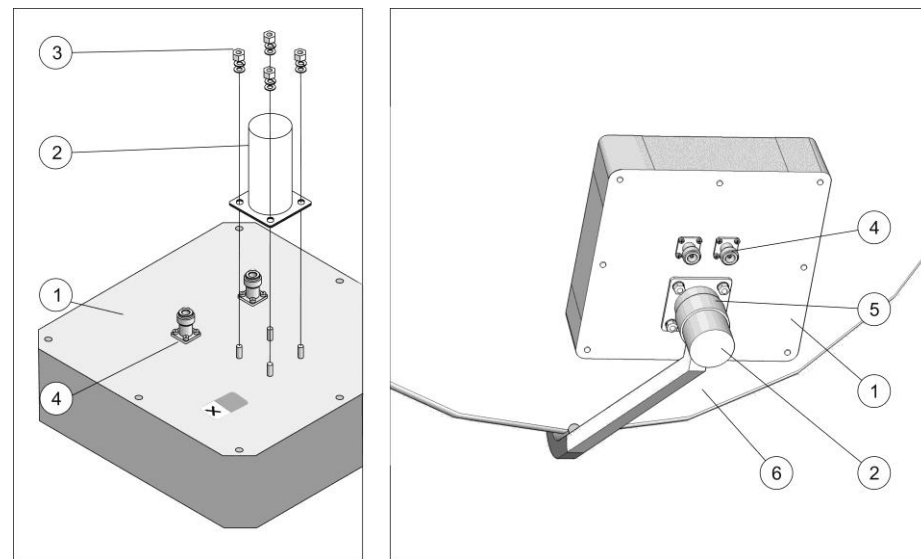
Сборка облучателя (слева) и установка в рефлектор (справа)
